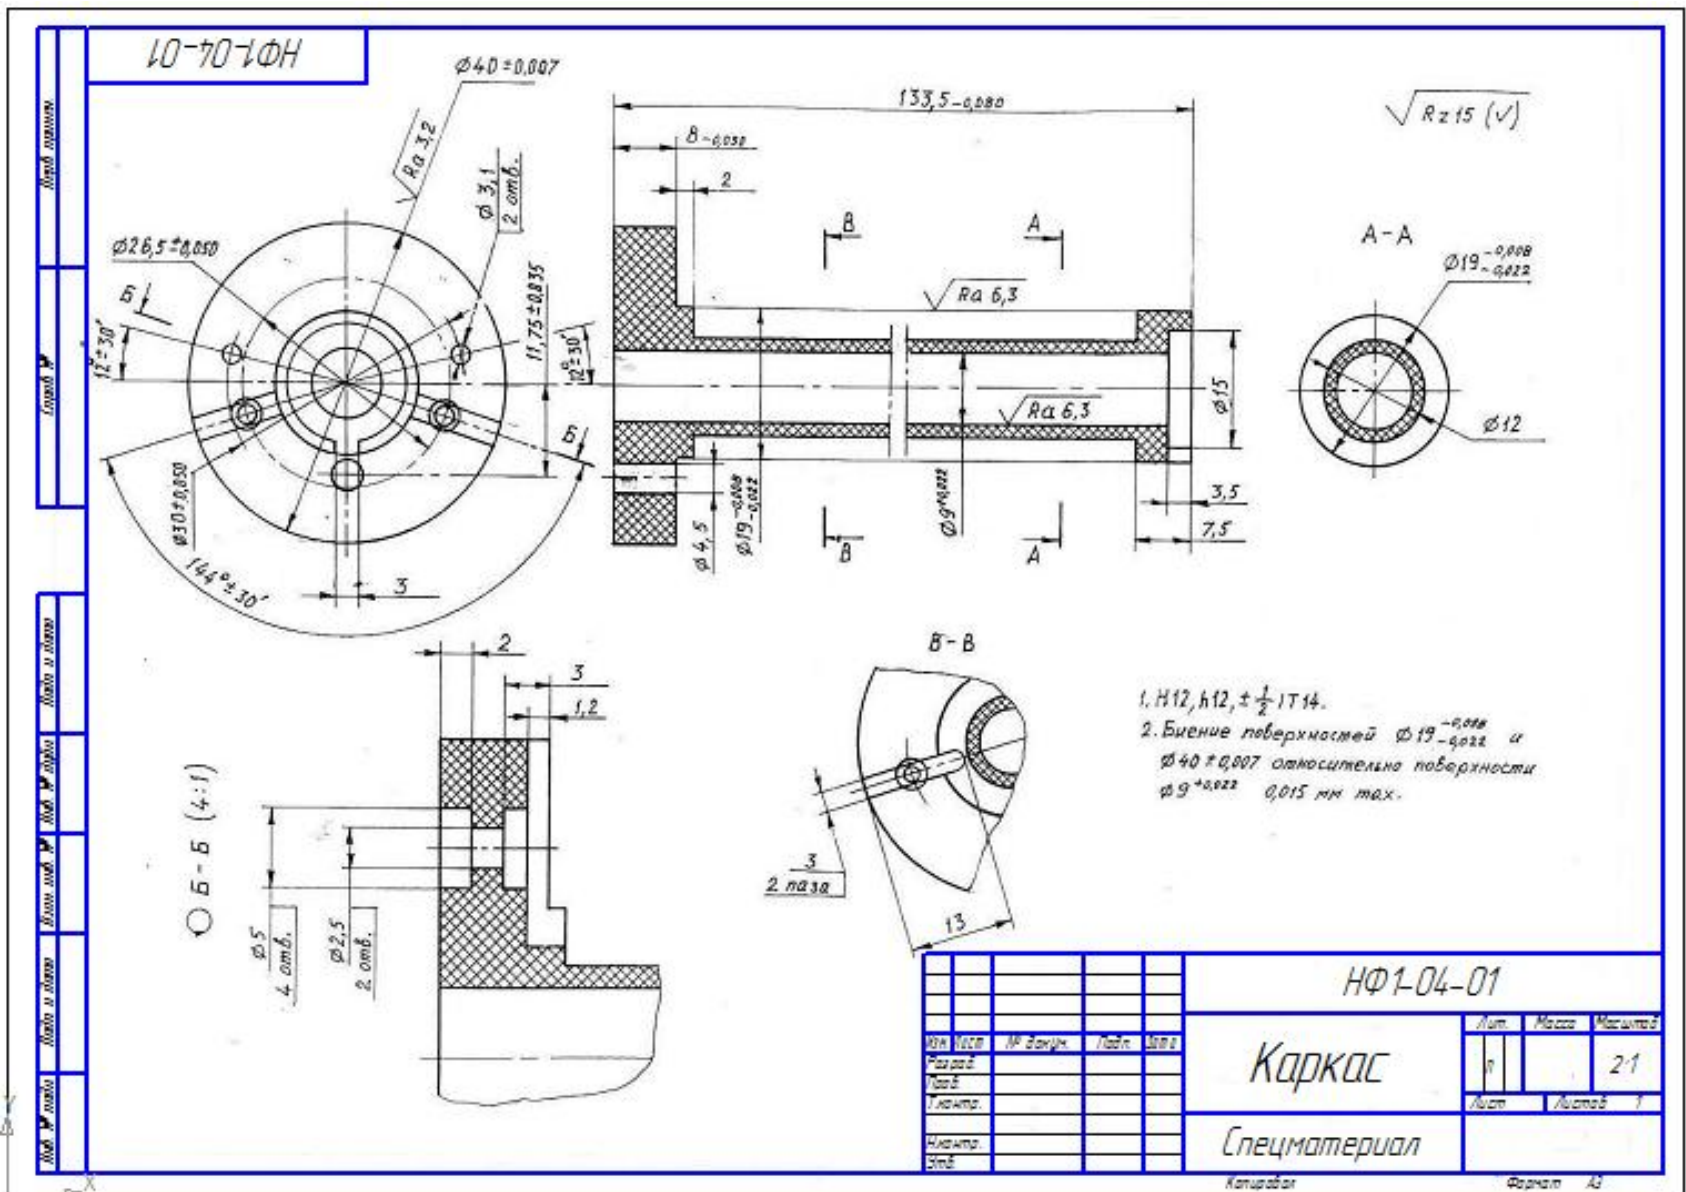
Пример выполнения рабочего чертежа детали «Каркас»
